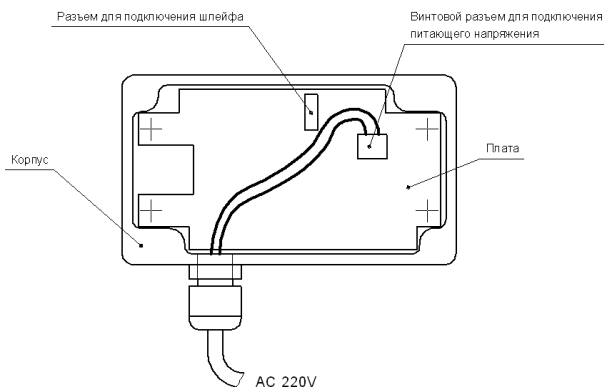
Схема подключения питающего напряжения к измерительному прибору WR-1-16
